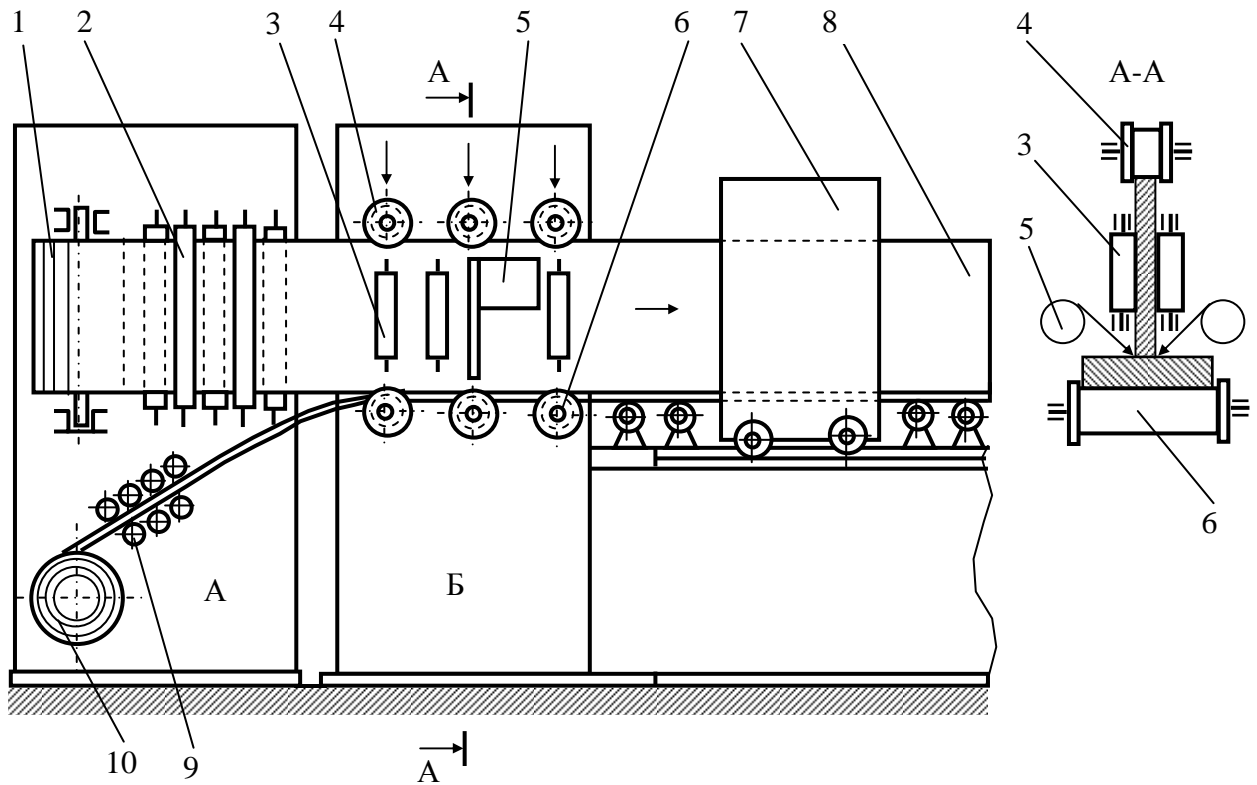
Схема комбайна для виготовлення балок електродуговим зварюванням: А-розмотувально-рихтувальна машина; Б-складально-зварювальна машина; 1, 10-рулони штабової сталі; 2, 9-виправлювальні вальці; 3-напрямні валки; 4-натискний валок; 5-зварювальна головка; 6-опорний валок; 7- летуча машина для розміреного обрізування "нескінченної" балки; 8-балка.
